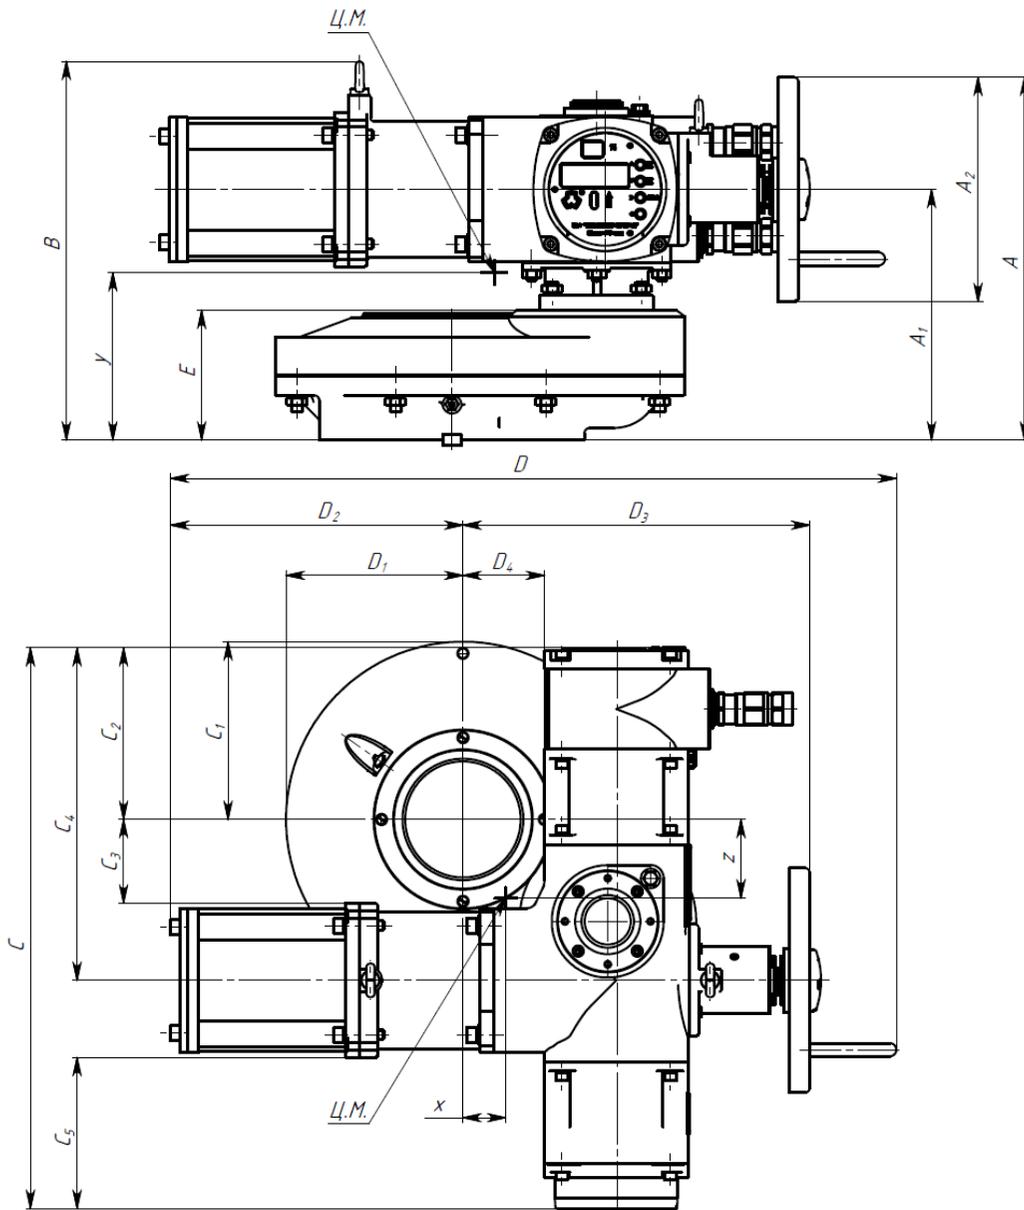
в – Габаритные размеры привода конструктивной схемы 410
